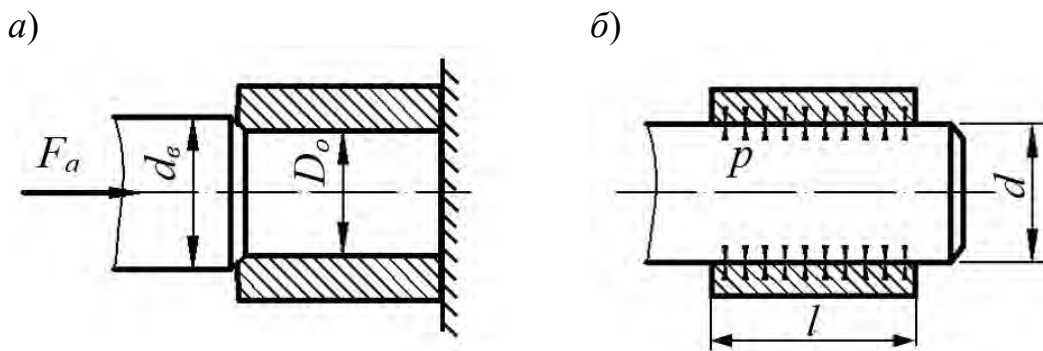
Образование соединения с натягом: а – перед запрессовкой; б – после запрессовки
